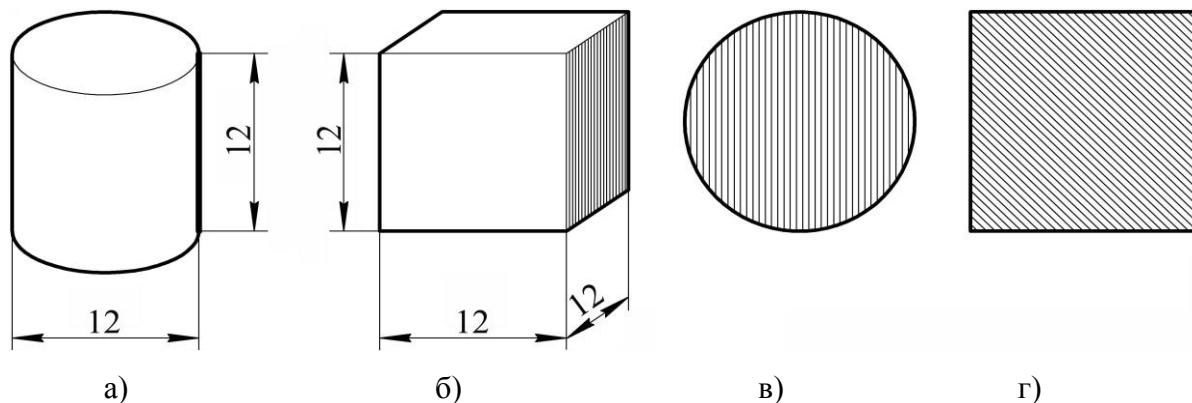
Общий вид металлических образцов: а-цилиндрические; б-прямоугольные; в и г-правильное расположение образцов в термической печи.
